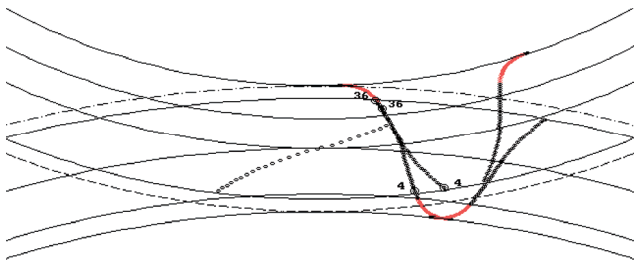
Зацепление профилей боковых поверхностей зубьев зубчатых колес с  $m = 5$ ,  $z_1 = 20$  и  $z_2 = 30$ , образованных инструментальными рейками 1 и 2 с выпукло-вогнутыми профилями боковых поверхностей зубьев
